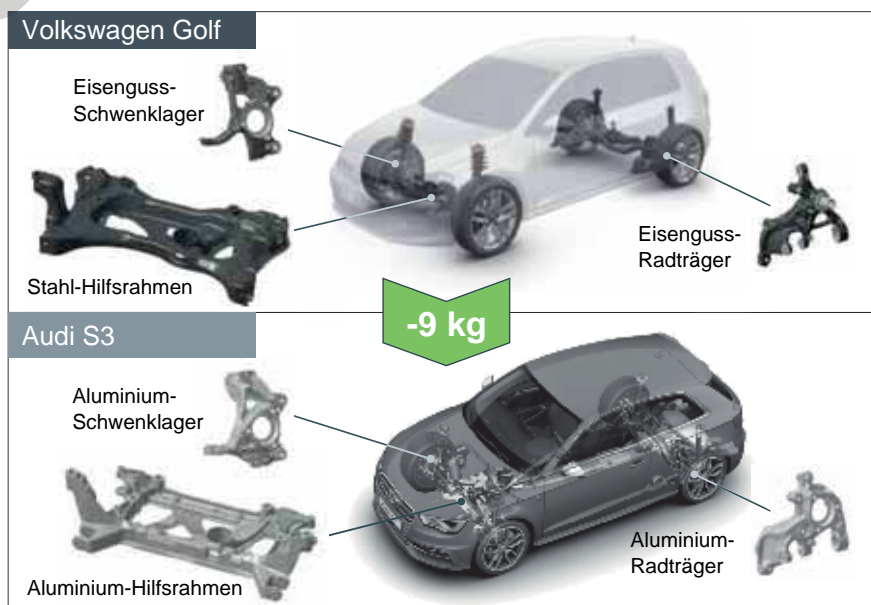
Klassenbezogene Leichtbaukomponenten aus Aluminium [1] im Vergleich mit Stahlguss- und Gusseisenkomponenten.
